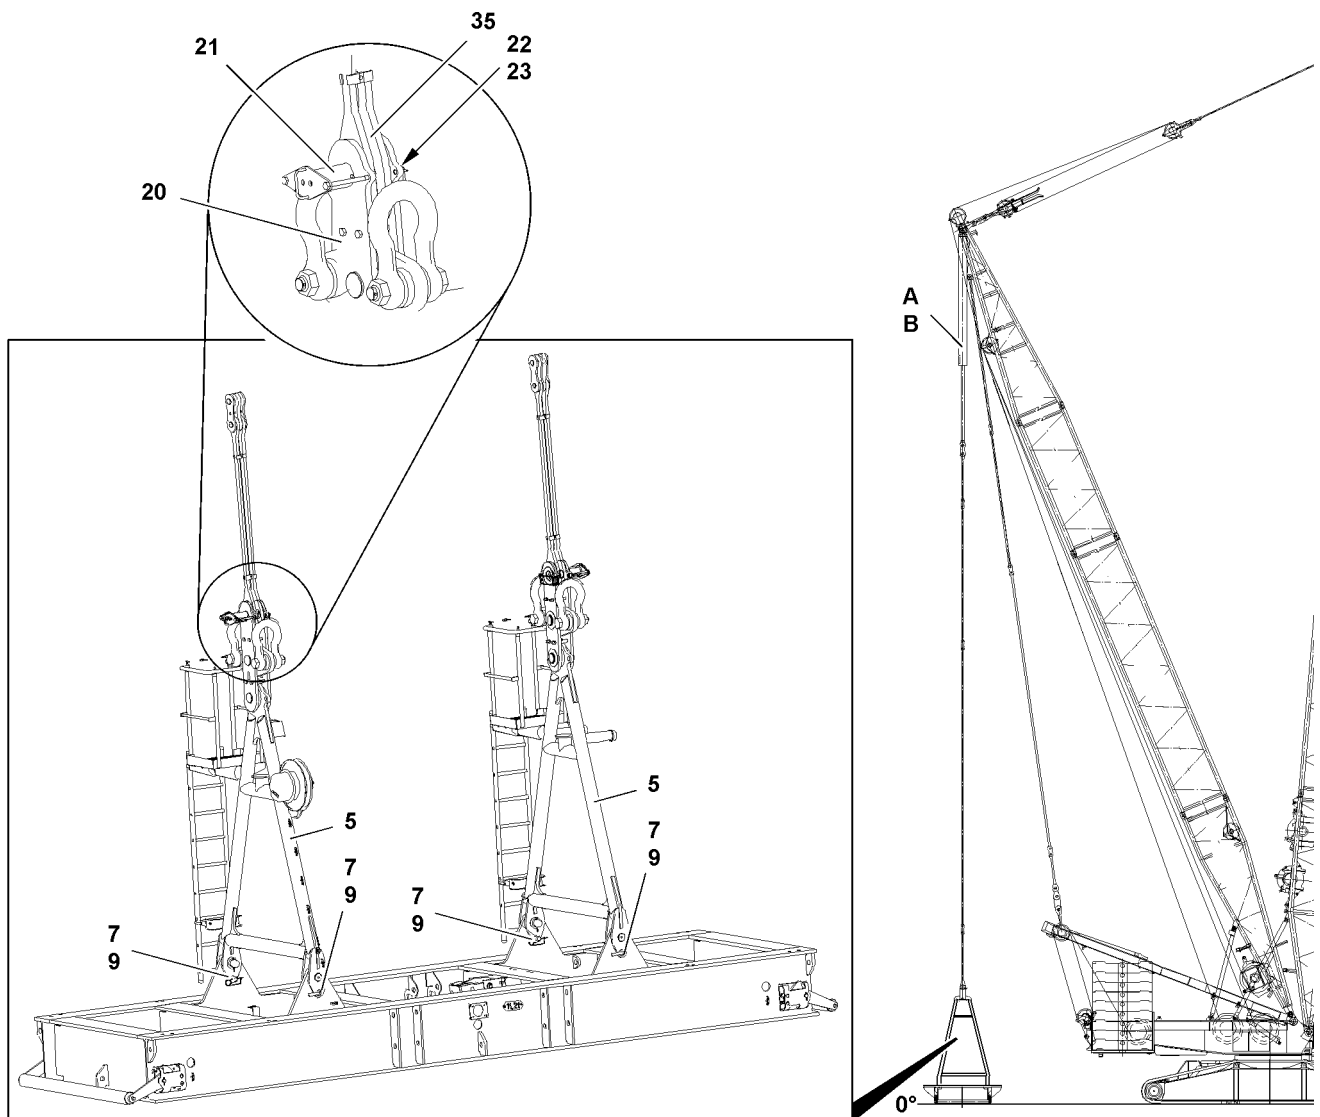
Desencavilhar a paleta do lastro em suspensão na barra de ancoragem D
